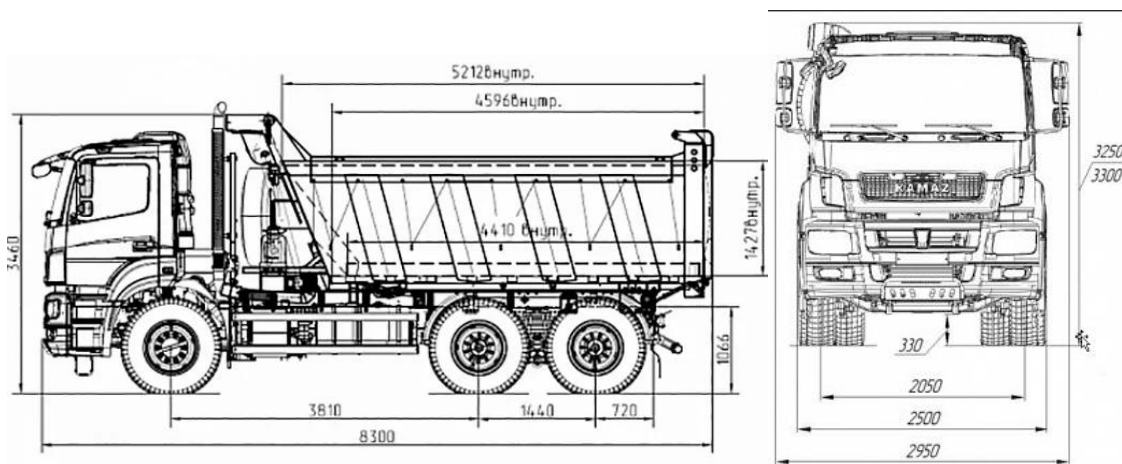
Основные конструктивные размеры автомобиля КАМАЗ 6580-S5
